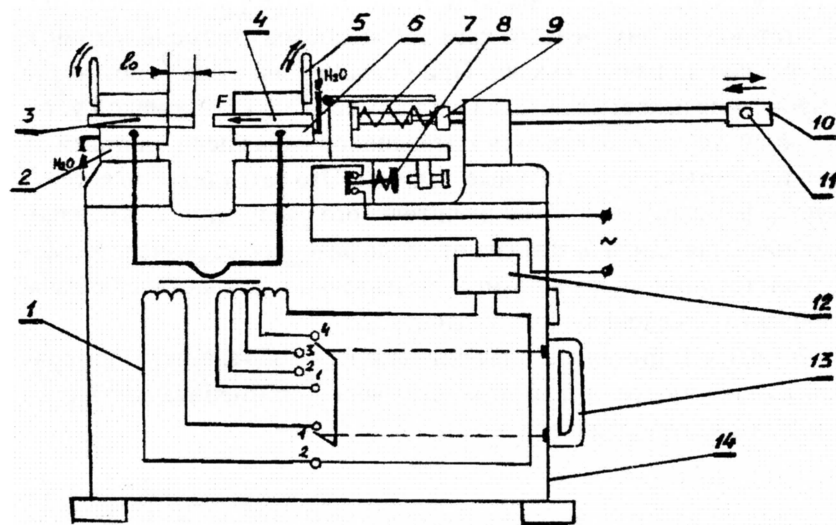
Электрокинематическая схема машины для стыковой сварки МСР-25:
